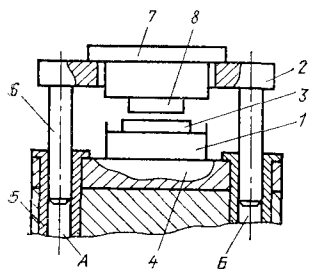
Принципиальная схема компоновки станка для электроэрозионной обработки крупногабаритных деталей
